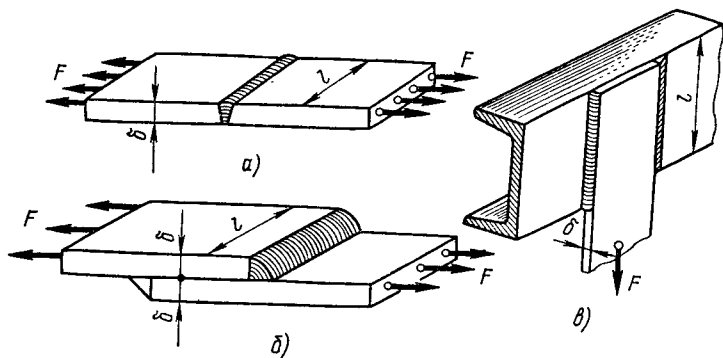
Сварные соединения, выполненные стыковым (а) и валиковыми лобовым (б) и фланговым (в) швами
